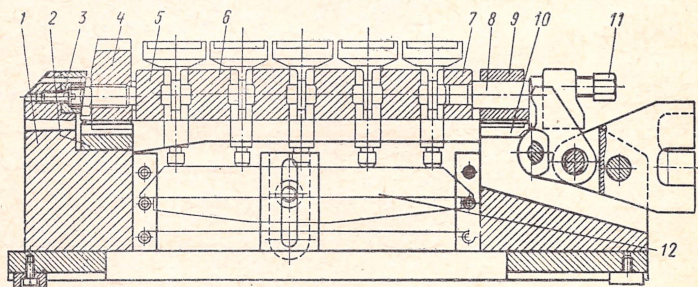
Универсальное кассетное приспособление для одновременной обработки группы деталей на фрезерном станке
